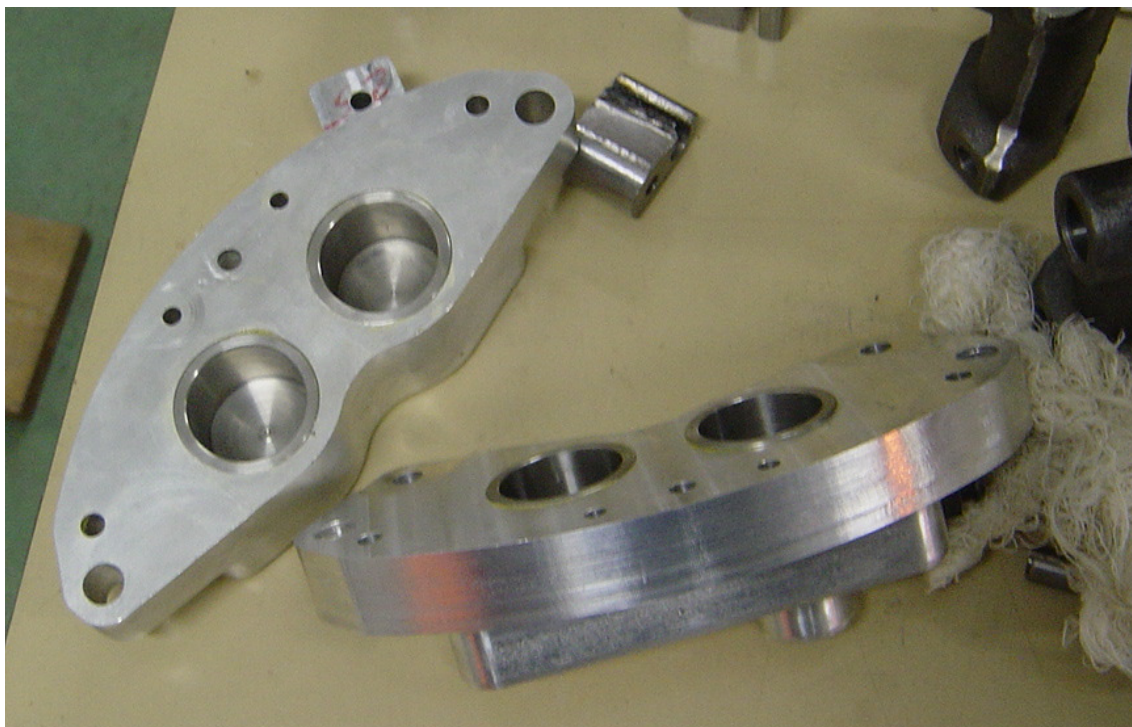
Pinça de freio fixa, quatro êmbolos, manufaturada pela Equipe. Projeto E1.³⁰
